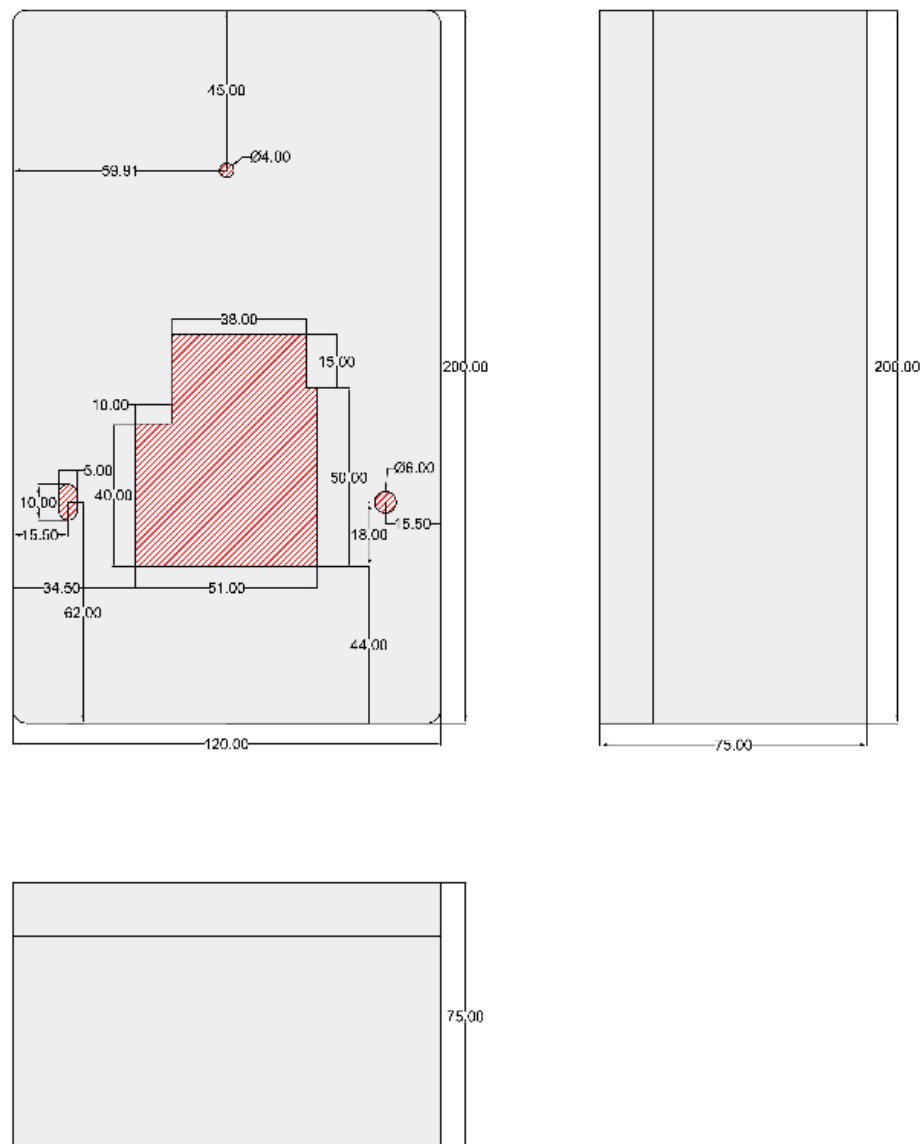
Alzado, planta y perfil de la caja contenedora con los agujeros necesarios (todas las medidas están en milímetros)
